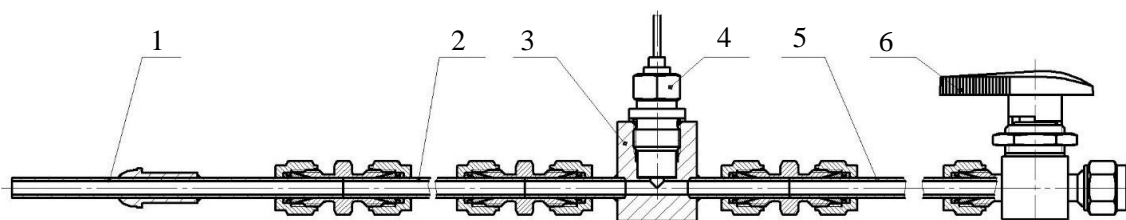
Конструкция опытного образца акустического зонда: 1 – входной участок волновода; 2 – сменный участок волновода; 3 – адаптер для установки датчика динамического давления; 4 – датчик динамического давления GTLab 5C101TA-400; 5 – согласованный трубопровод; 6 – кран.
